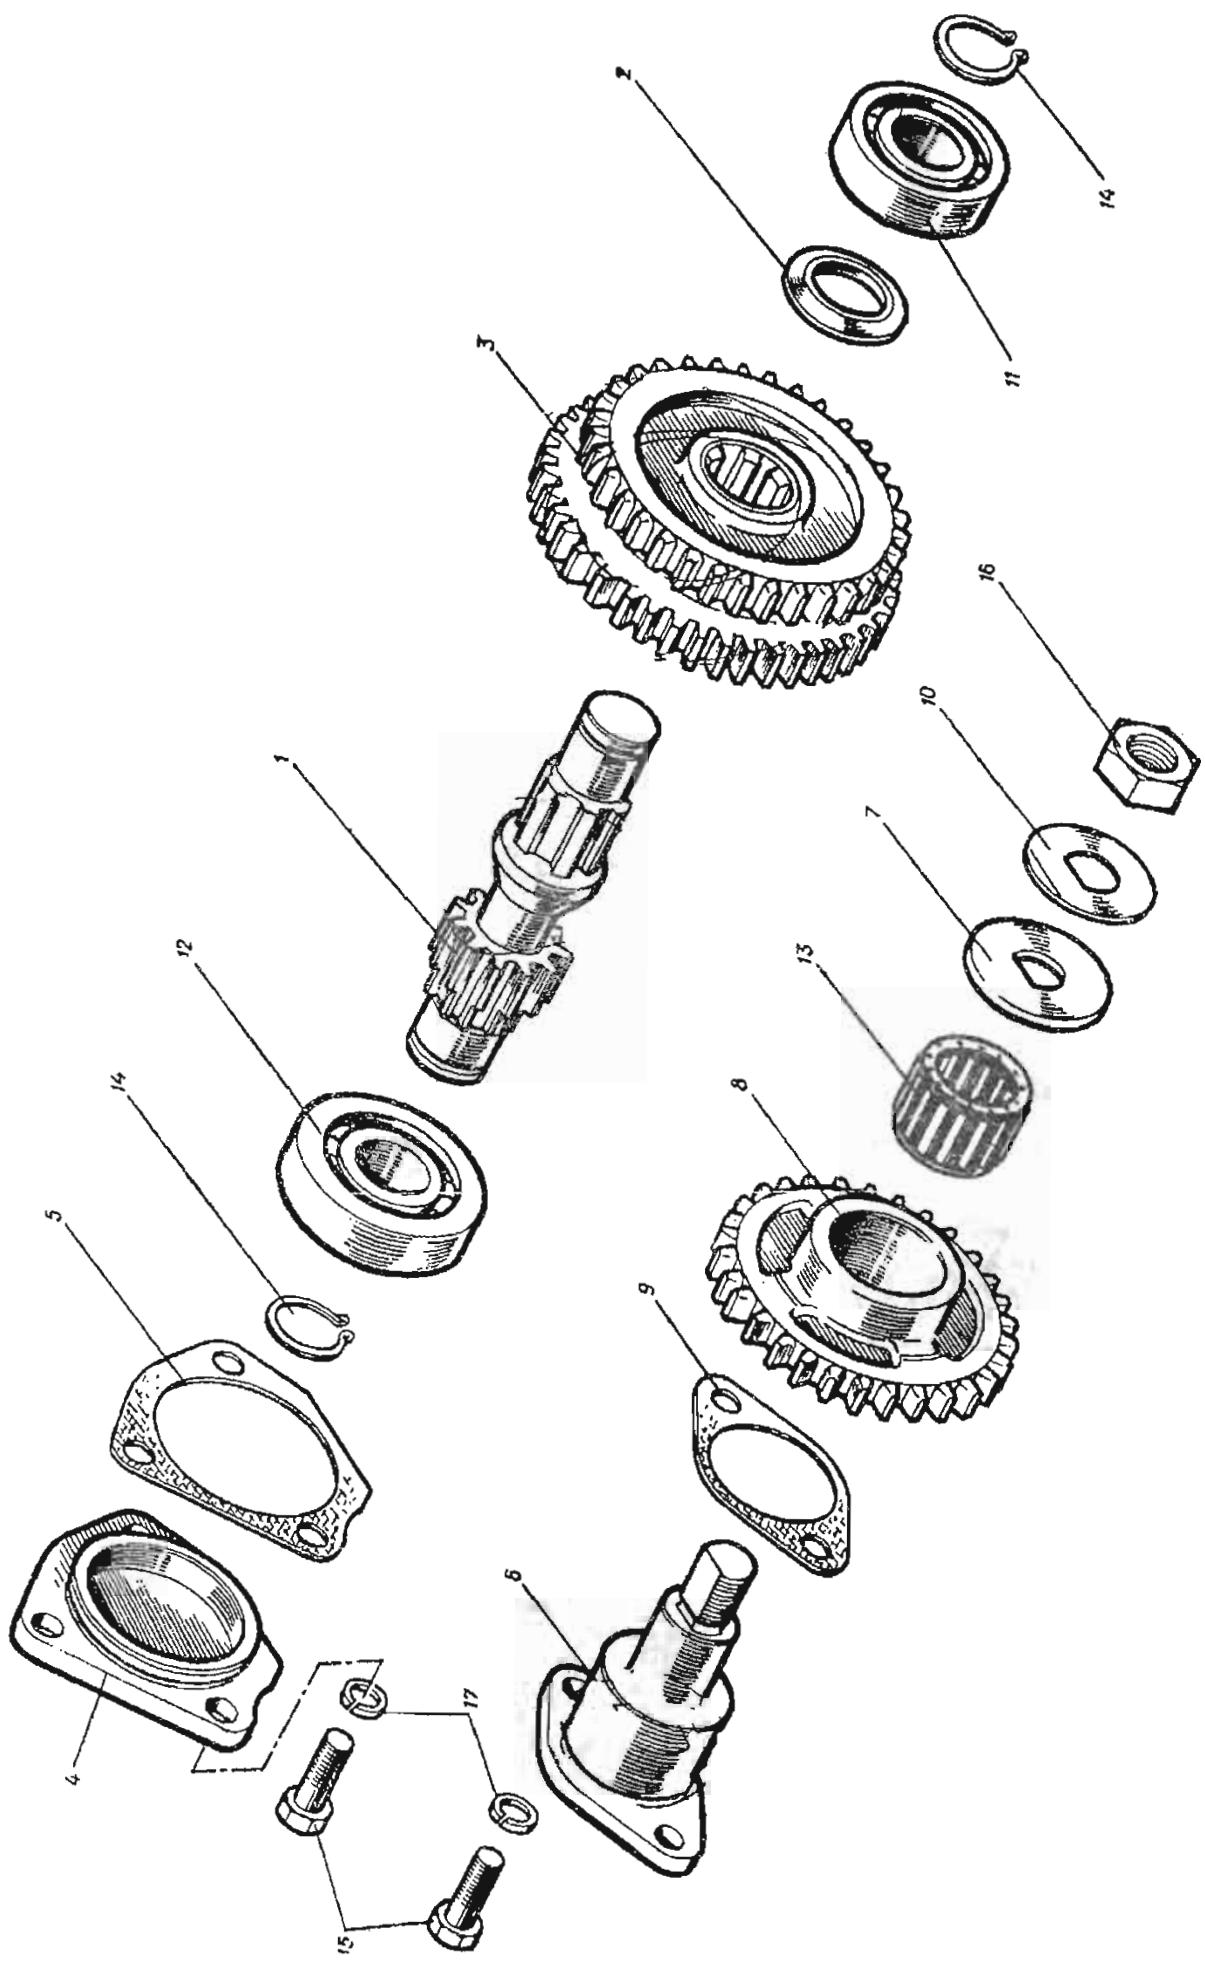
Коробка перемены передач (детали дополнительной передачи и заднего хода)
